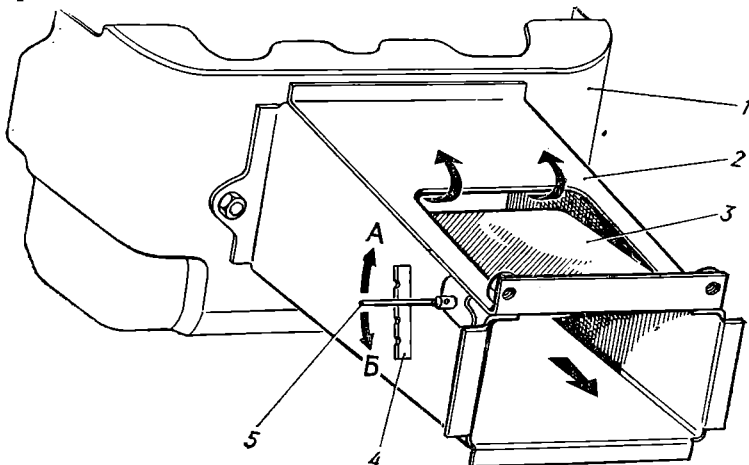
Кожух воздухоотводящий двигателя МеМЗ-966Г:
